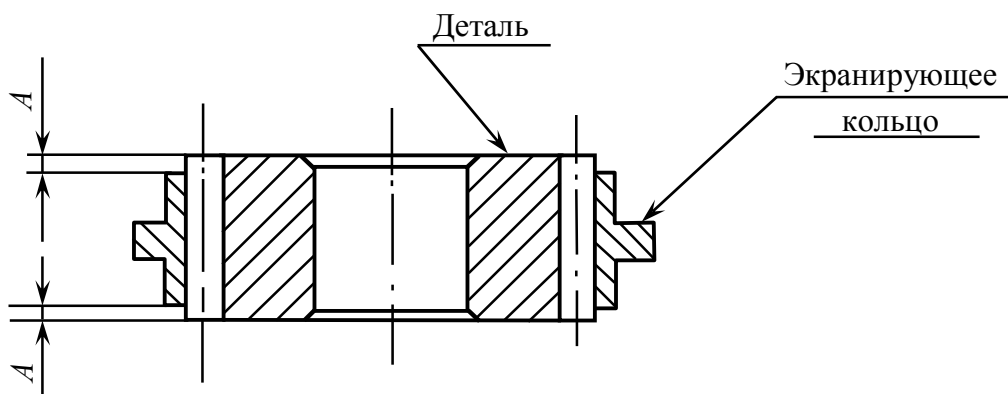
Схема установки экранирующего кольца на обрабатываемую деталь
